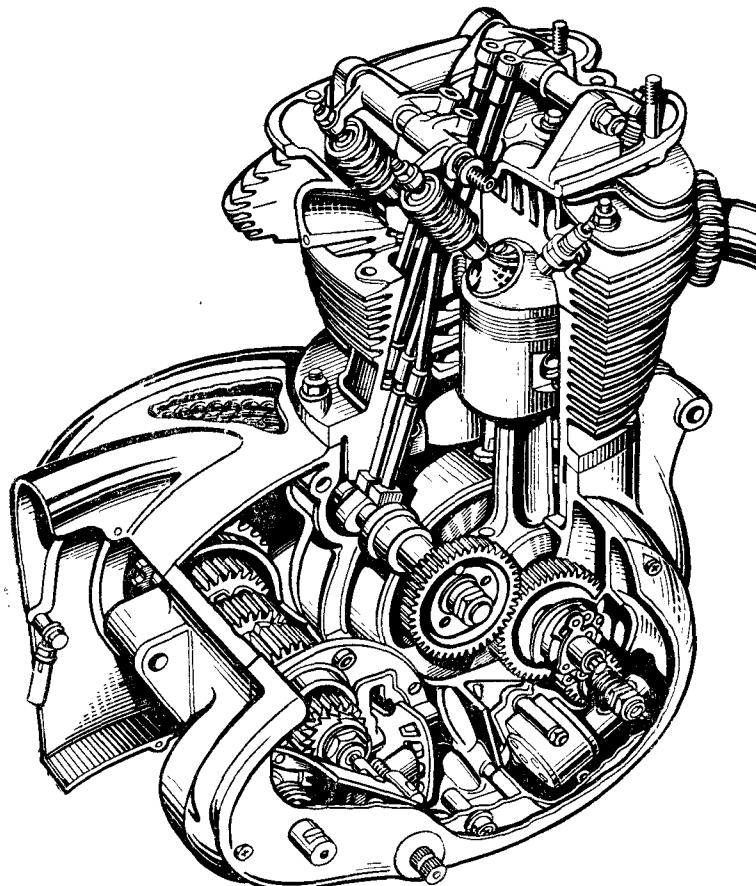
Двигатель BSA-650 со штанговым приводом клапанов
